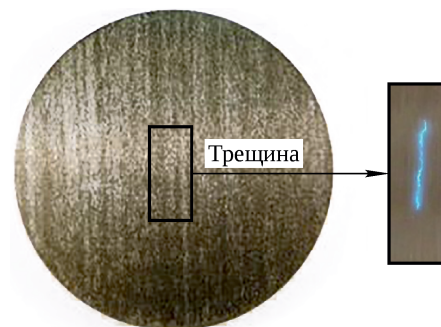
Образец с усталостной трещиной на плоской поверхности для тестирования капиллярного и вихретокового контроля [10]
